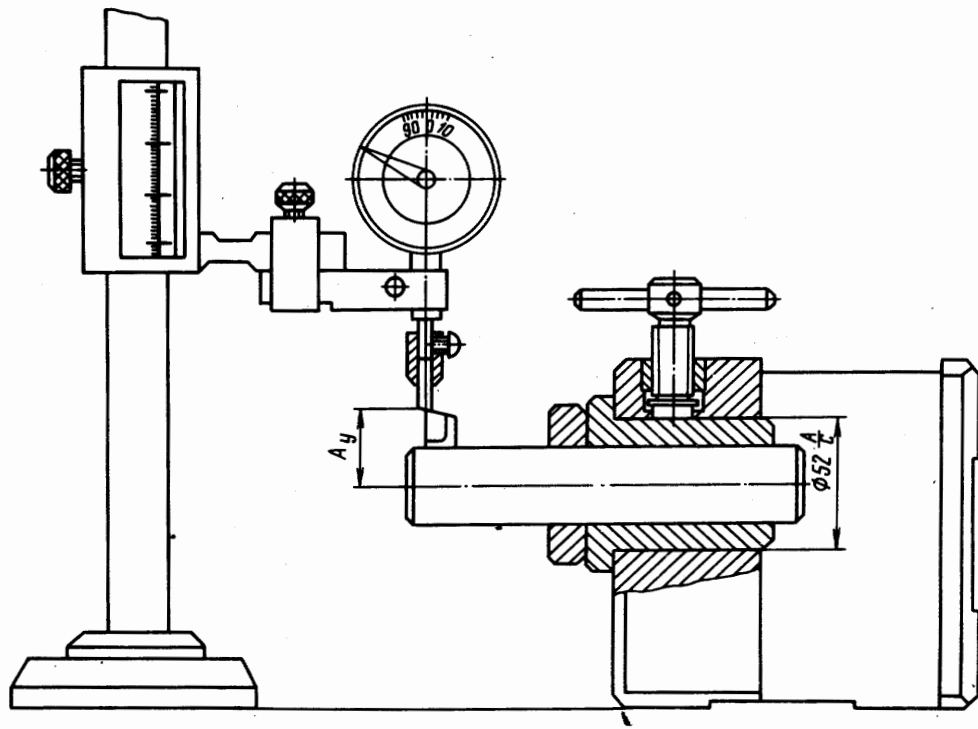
Схема наладки инструмента вне станка. Установка диаметрального размера
